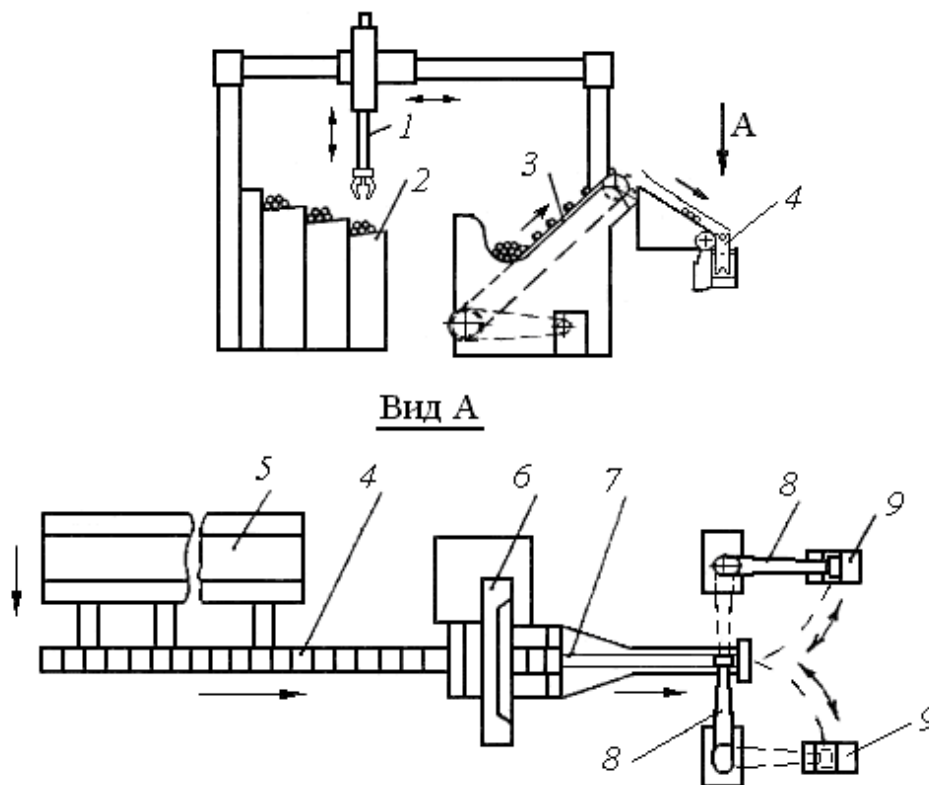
Схема РТК для разделения сортового проката (прутков) на мерные заготовки:
